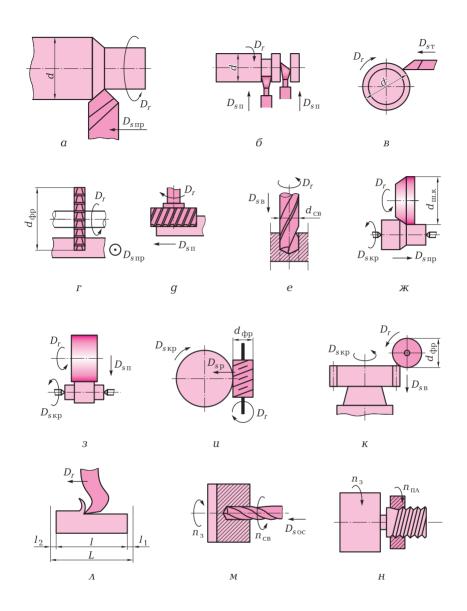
Виды главного движения и движения подач в токарных (a, 6, 8), фрезерных (r, д), сверлильных (e), шлифовальных (x, 3), зубофрезерных  $(u, \kappa)$ , строгальных (n) станках и токарных автоматах (m, h):
